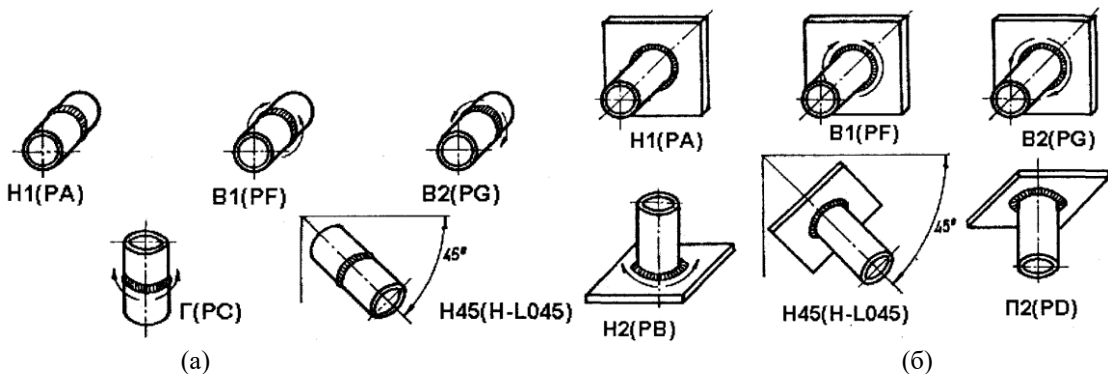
Положения при сварке стыковых (а) и угловых (б) соединений труб:
